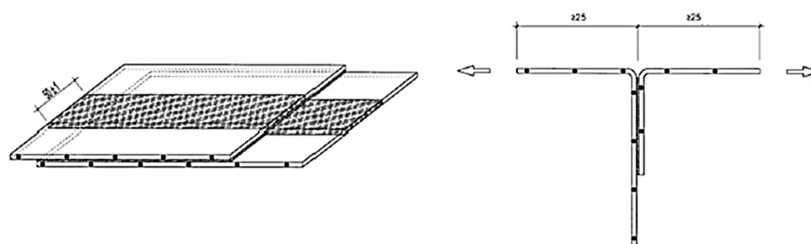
Esquema de la probeta utilizada para determinar la resistencia de la soldadura por pelado
